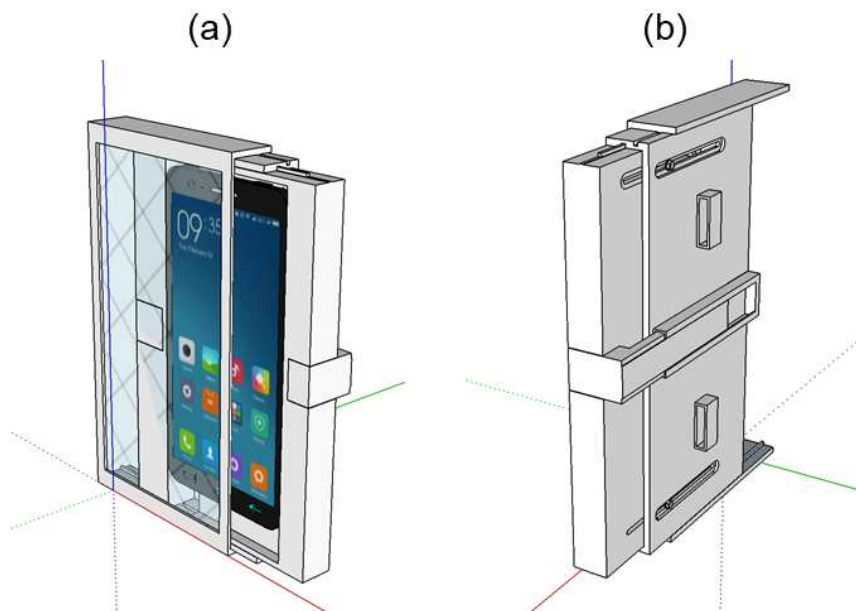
Schémas du dispositif d'attache : (a) Vue de devant ; (b) Vue de derrière - Dessins Marc Vanderweyen
